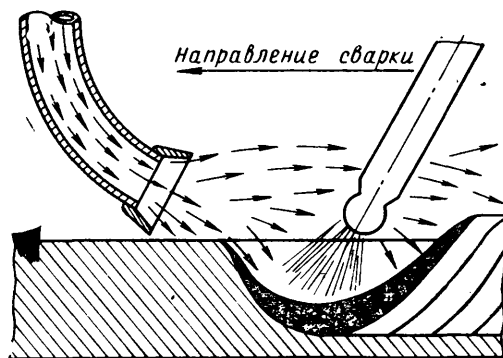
Схема процесса сварки с боковым подводом углекислого газа
